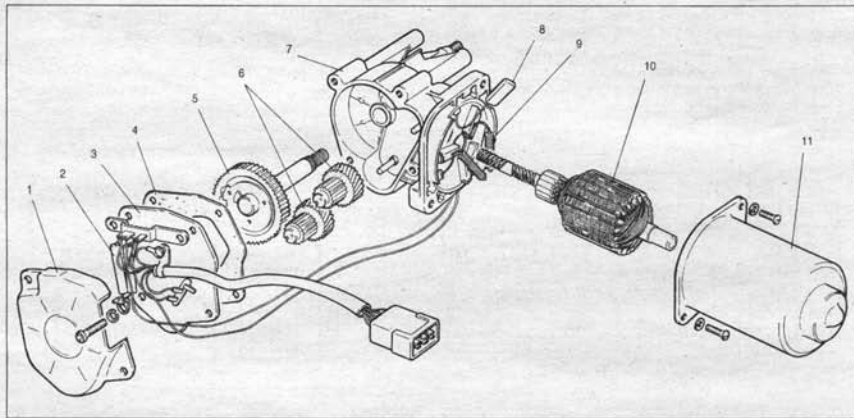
Детали моторедуктора очистителя ветрового стекла:
